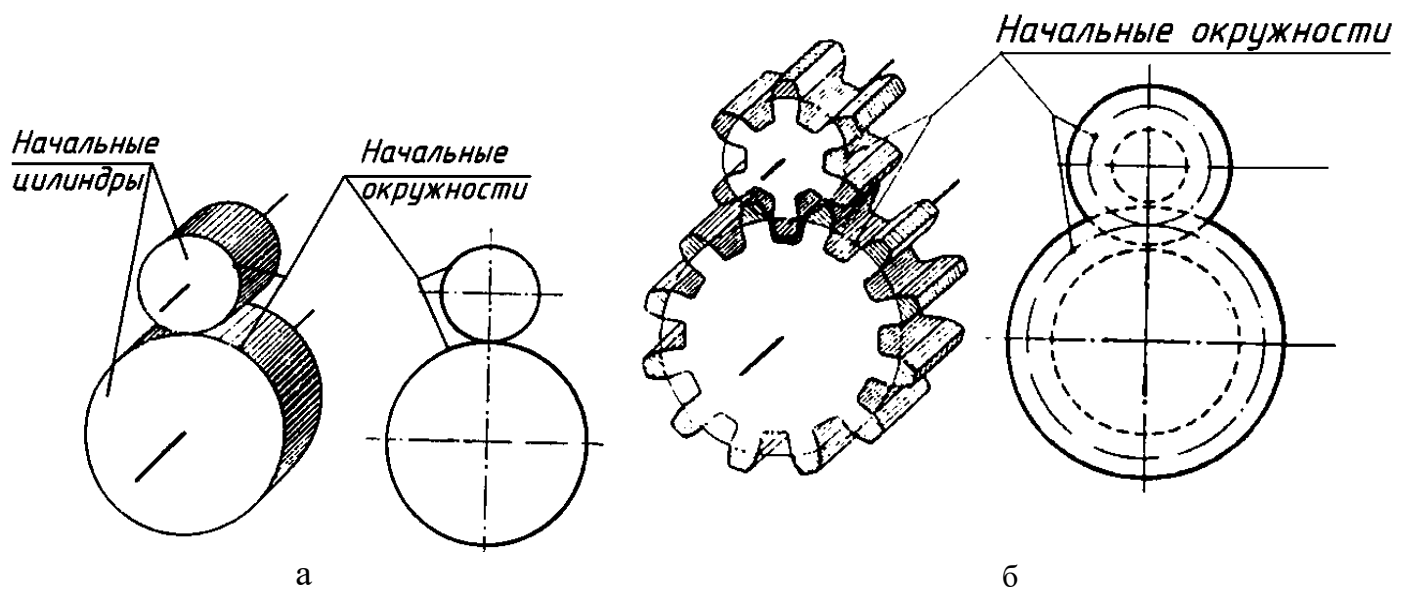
Образец выполнения чертежа зубчатого зацепления.
